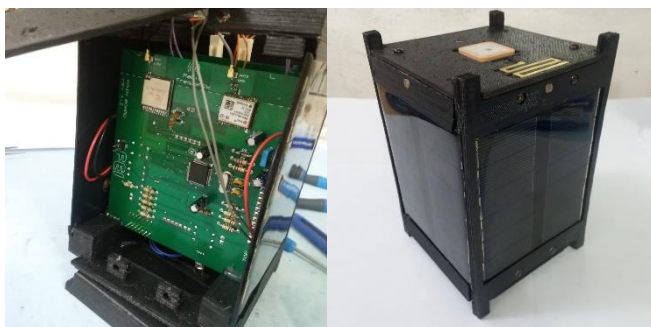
Esq. vista interna da fixação da placa principal. Dir. montagem final do LCP.
